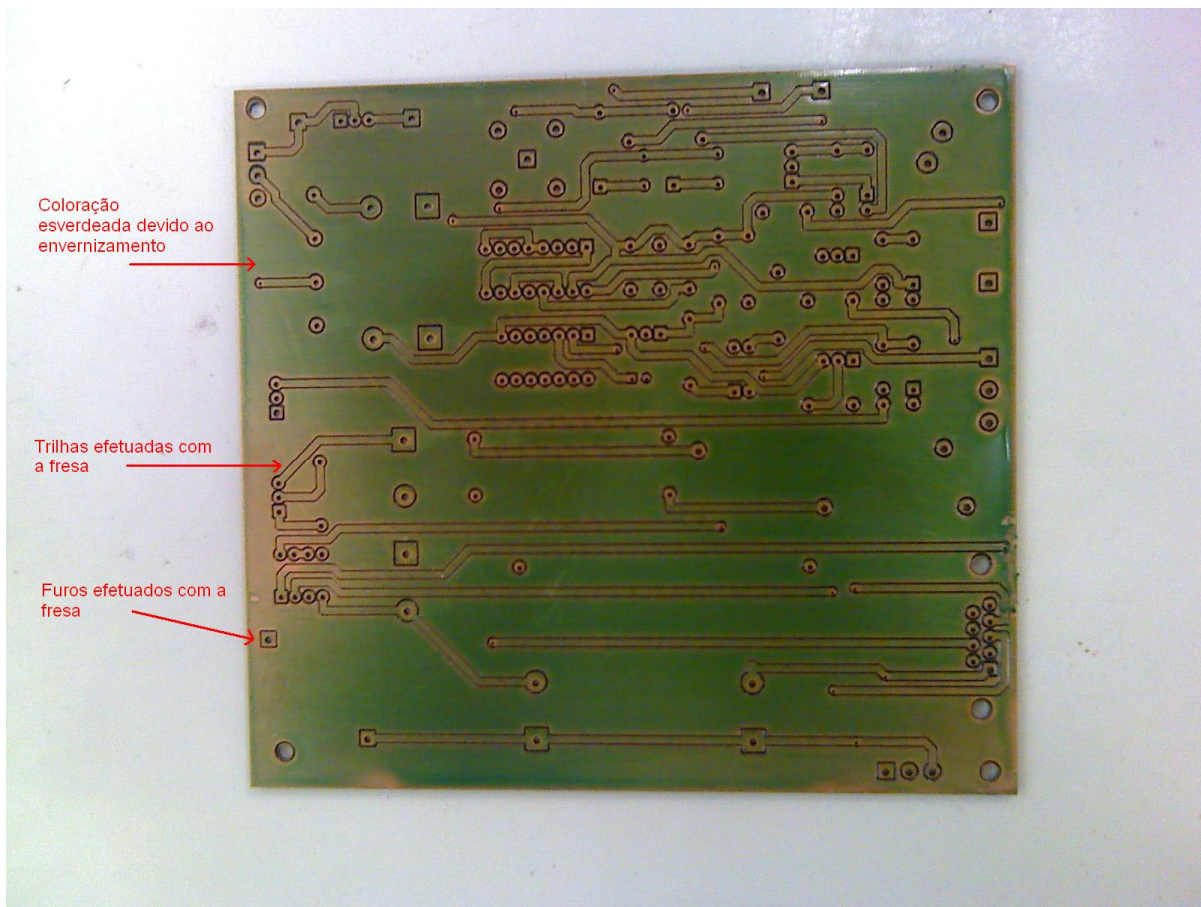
Placa de circuito impresso confeccionada pelo processo de fresamento e metalização.
